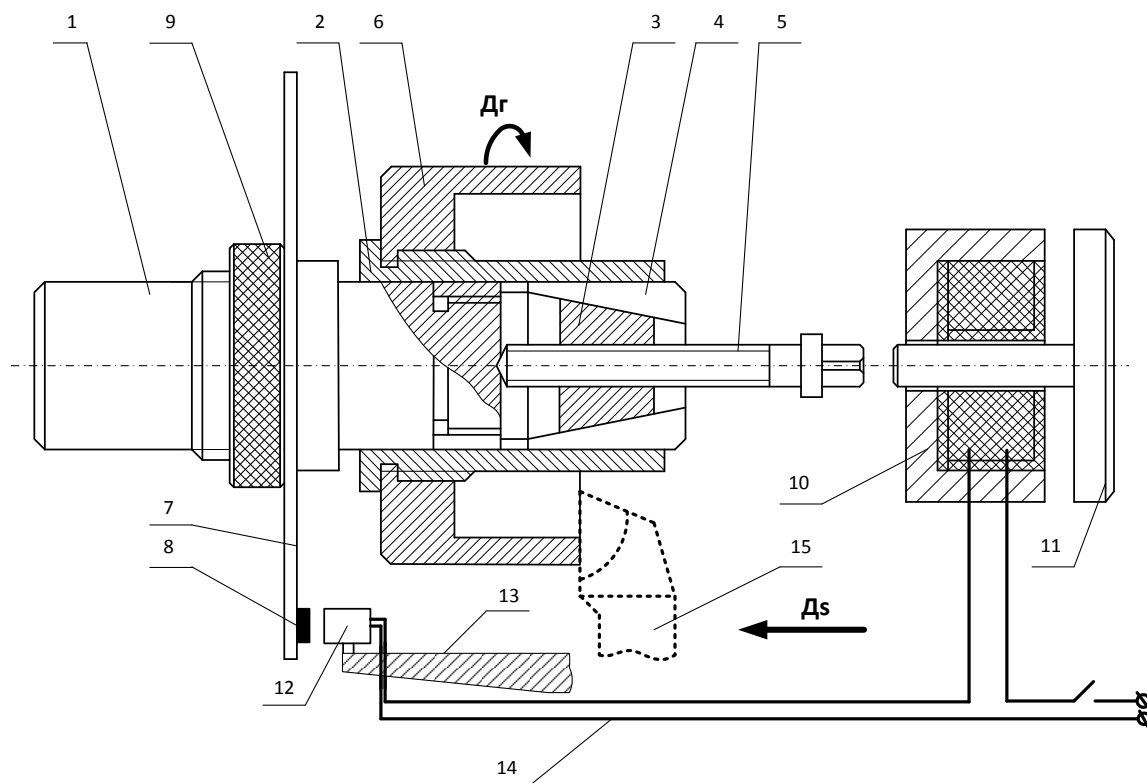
Цанговое приспособление для мгновенного прекращения резания: 1- корпус; 2 – втулка; 3 – конус; 4 – цанга; 5 – винт; 6 – образец; 7 – диск; 8 – магнит постоянный; 9 – контргайка; 10 – электромагнит; 11 - сердечник электромагнита; 12 – геркон; 13 – штанга; 14 – электрическая цепь; 15 - резец
